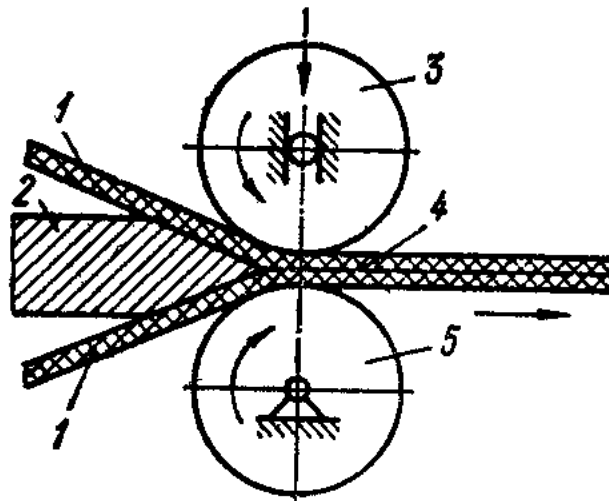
Схема зварювання нагрітим клином: 1-плівки; 2-клиноподібний нагрівний інструмент; 3,5-ролики; 4-зварний шов.
